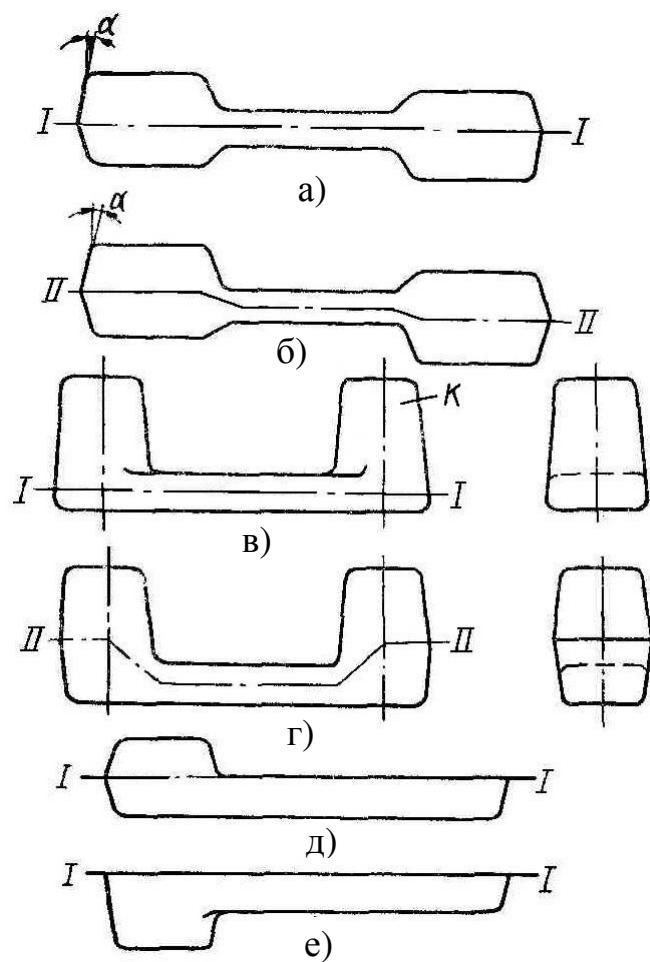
Роз’єднання штампів для довгих поковок:
